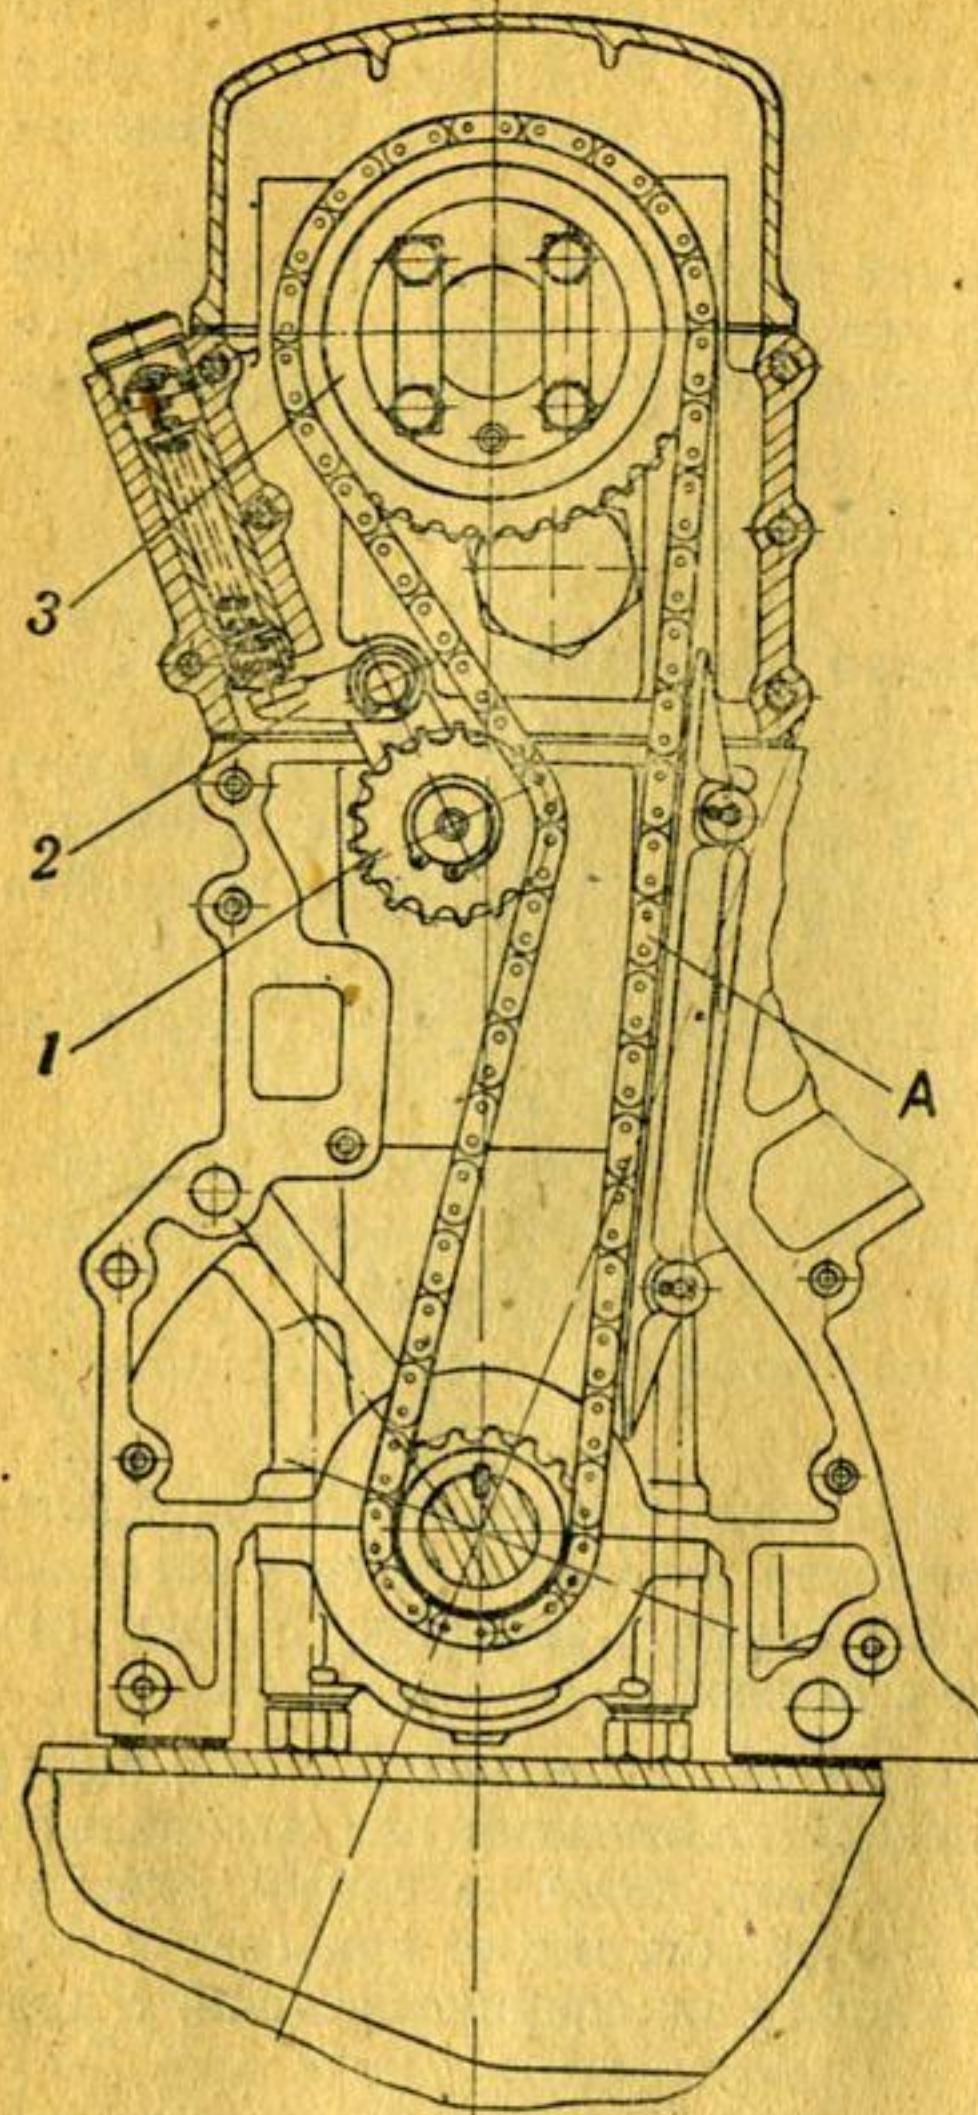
Схема механизма натяжения цепи привода распределительного вала:
